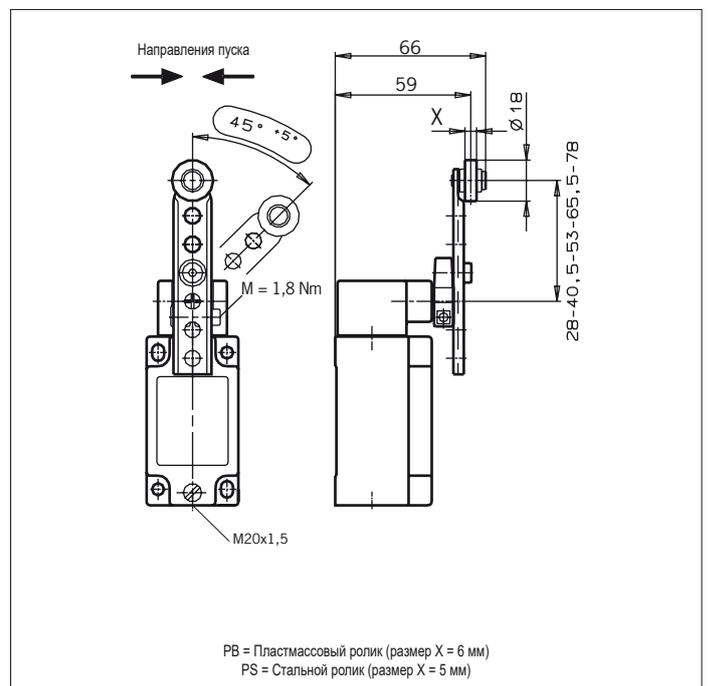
Размерный чертеж NZ1P... с кабельным вводом
